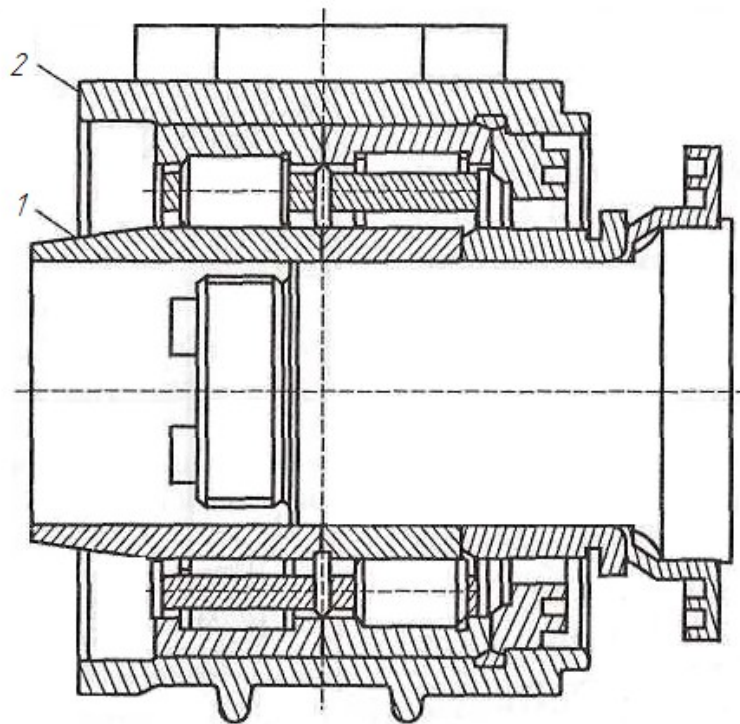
Розташування букси з підшипниками при установленні на шийку осі з розтискною втулкою
